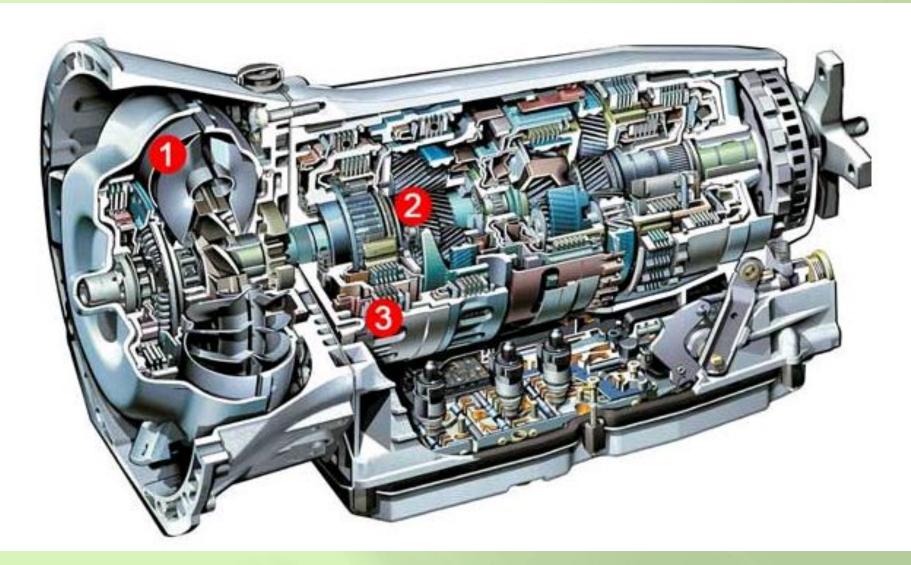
Автоматическая коробка передач: 1 – гидротрансформатор; 2 – планетарный редуктор; 3 – сцепления-фрикционы
